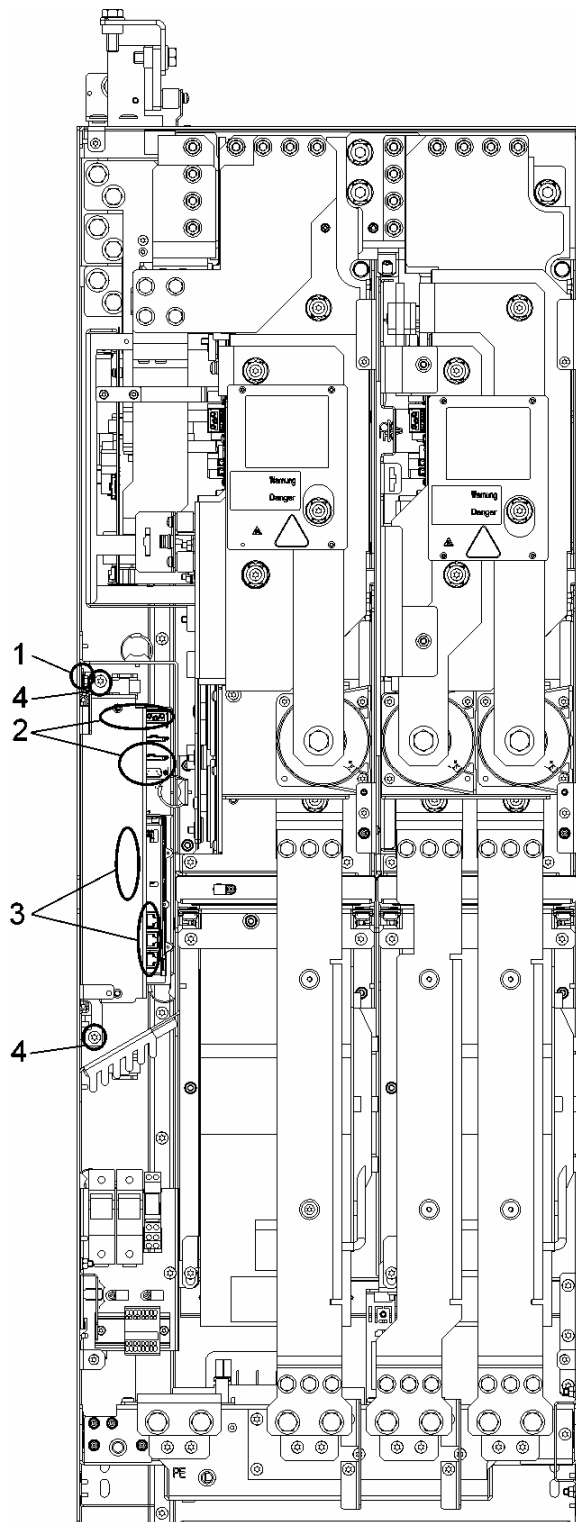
Замена платы Control Interface Board, типоразмер НХ
